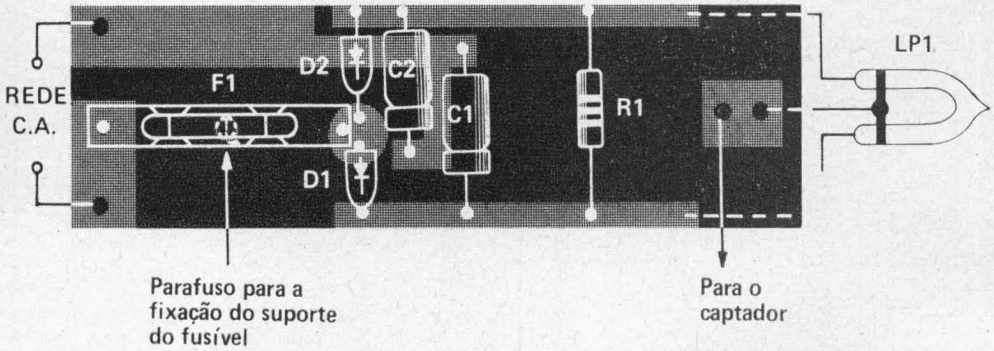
Disposição dos componentes sobre a plaqueta da Fig. 2.
